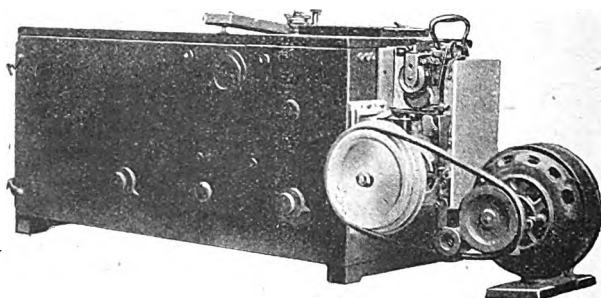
Dimensions d'encombrement : 770×350 mm, haut : 345 mm.
